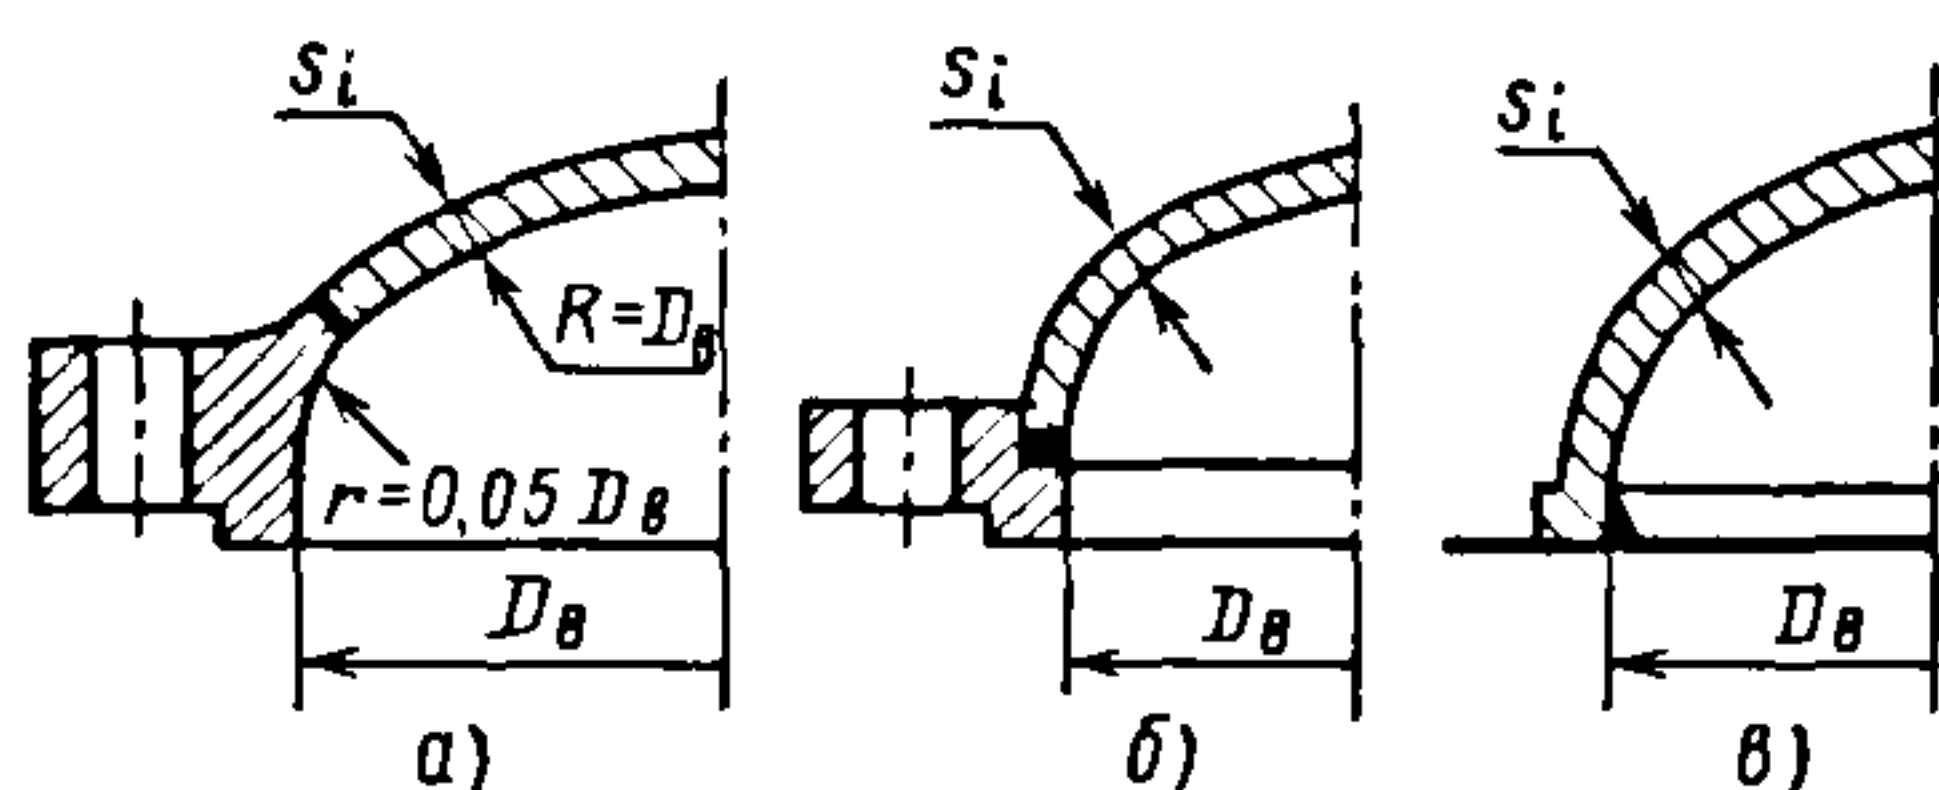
Сварные крышки больших диаметров:
